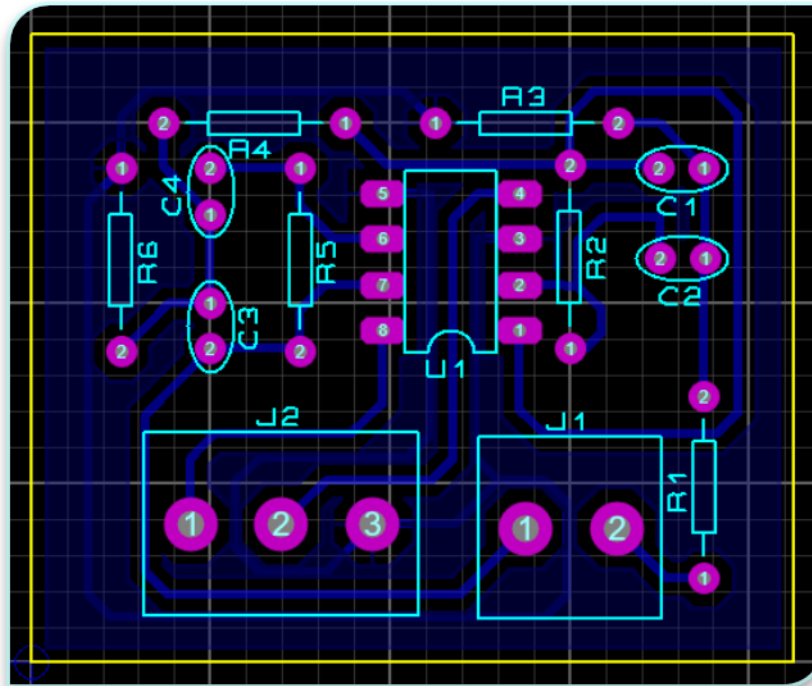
Diseño de la etapa de filtrado sobre PCB en Ares.
